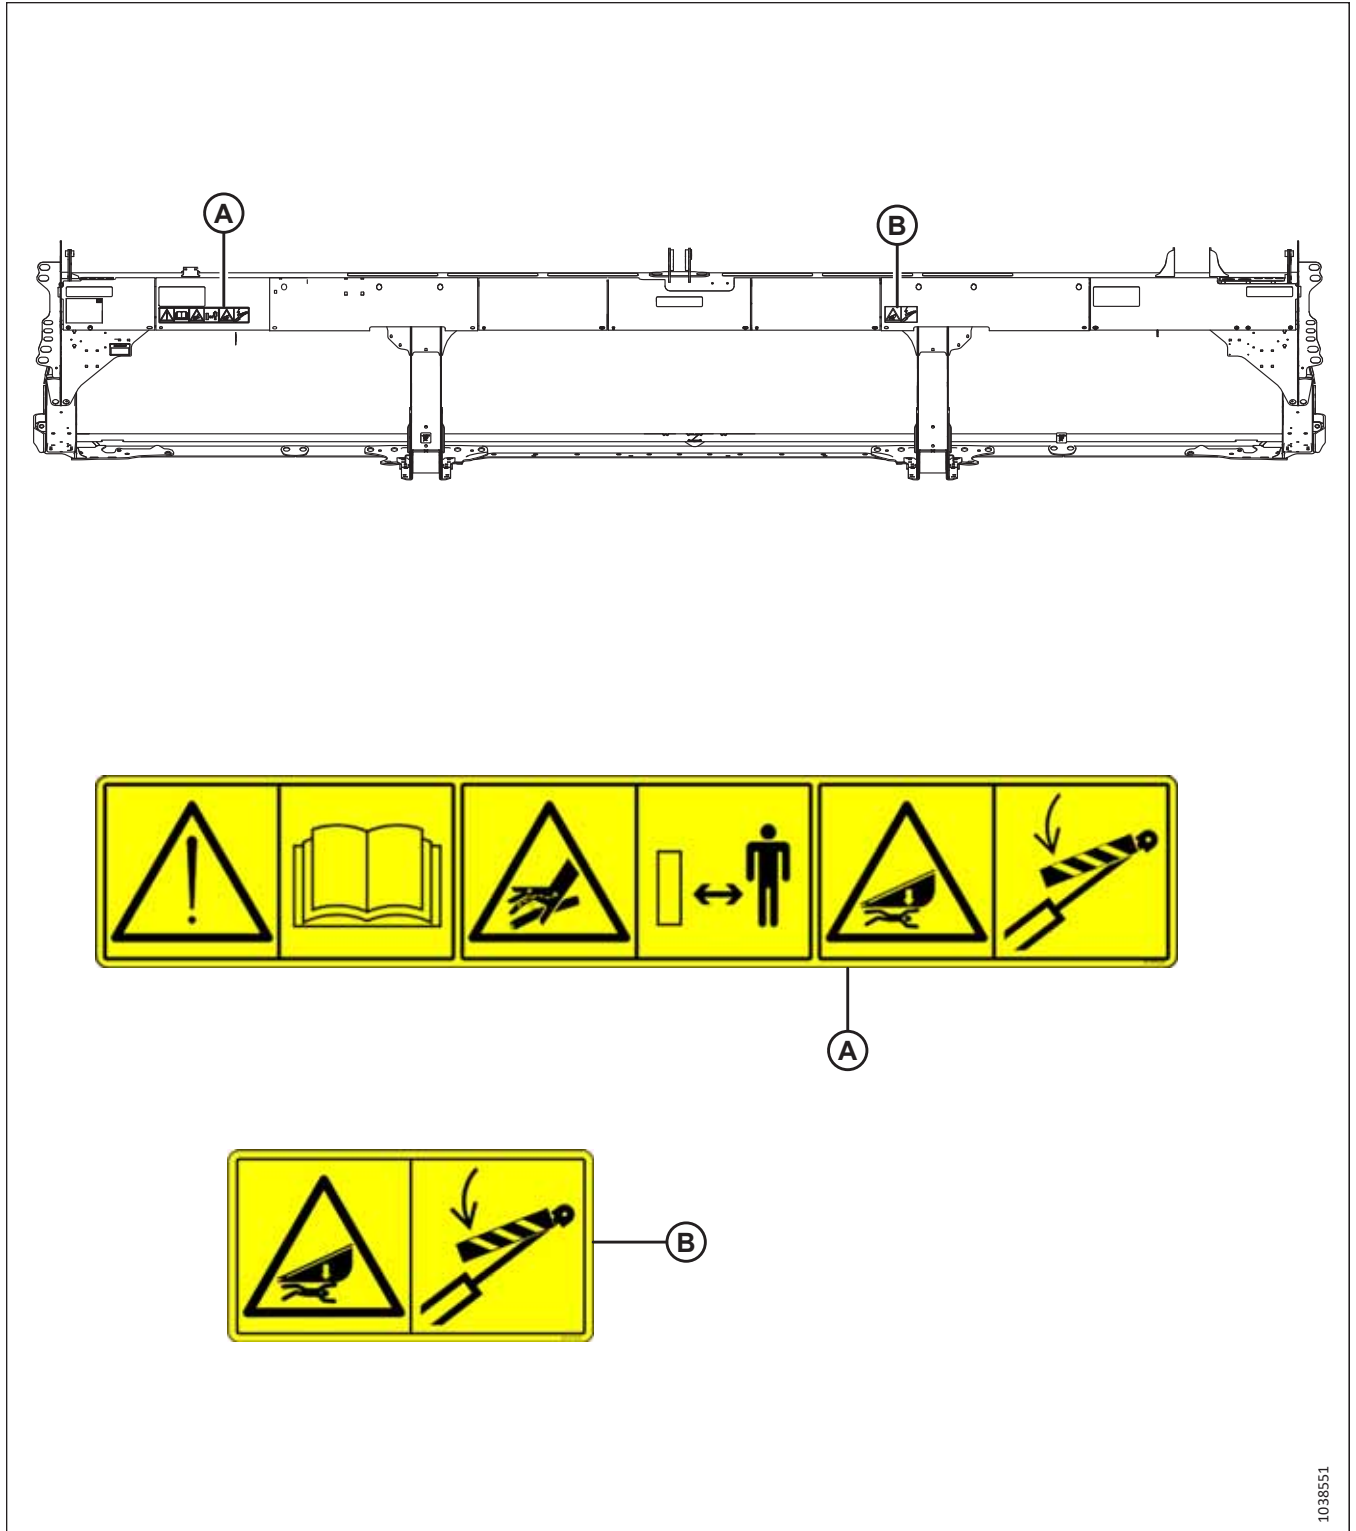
Tube arrière – Plateforme de coupe à tapis D220
